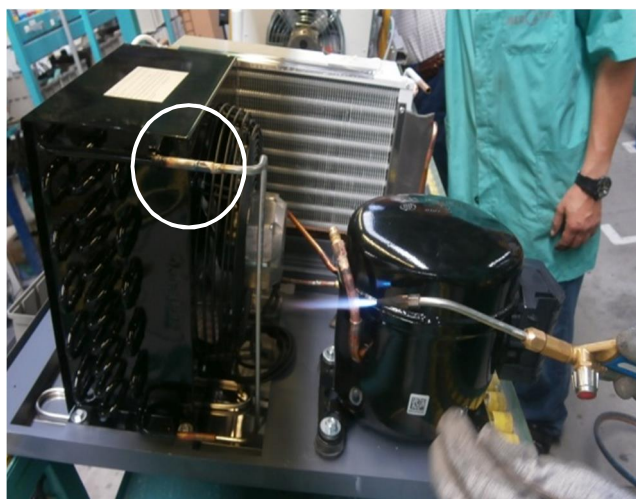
Operação de soldadura condensador - serpentina
